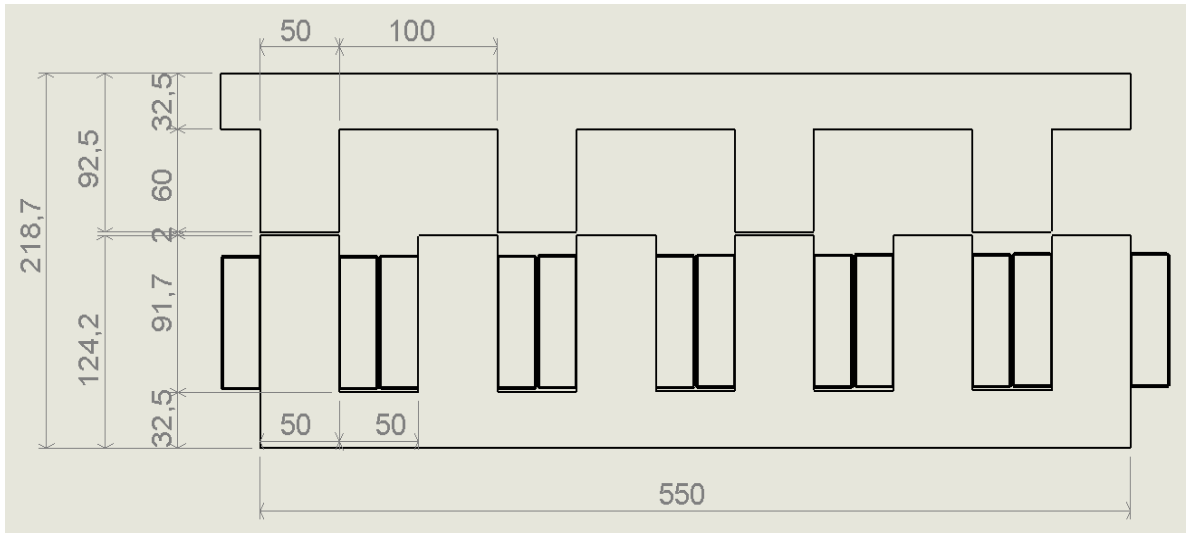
Principais dimensões gerais do gerador linear planar [20]
